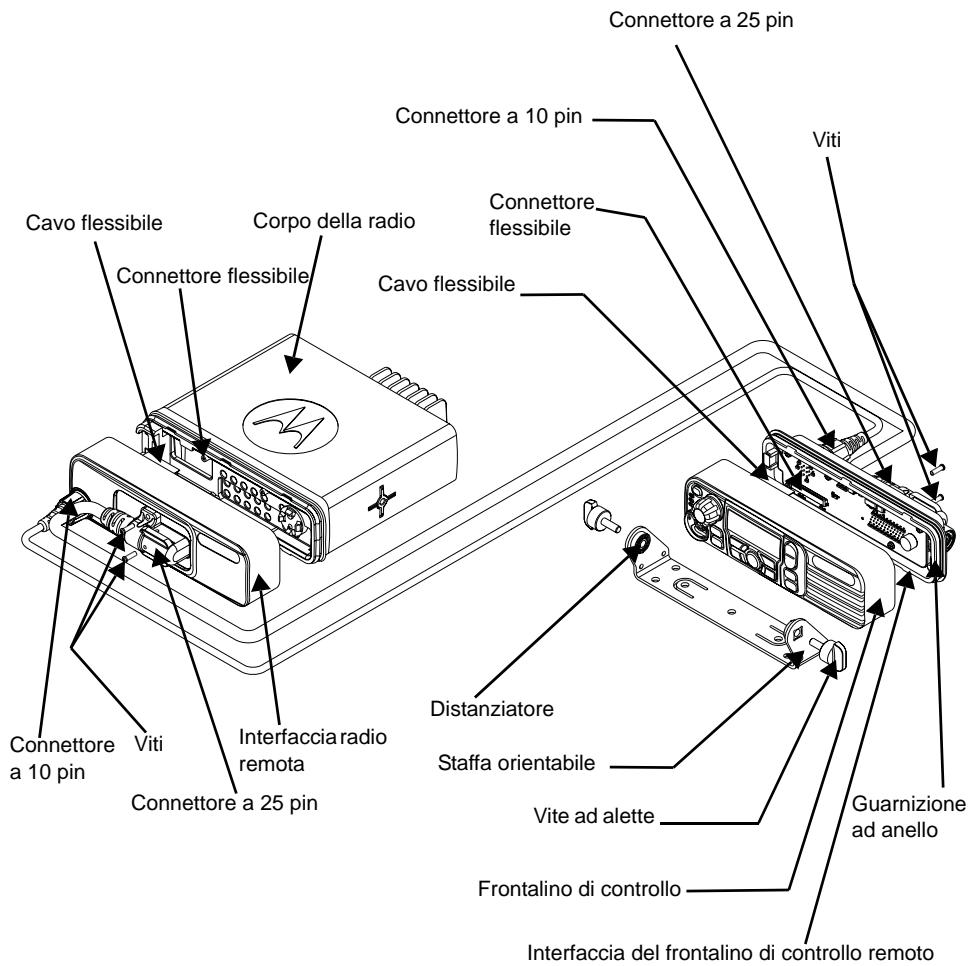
Montaggio del frontalino di controllo remoto e della staffa
